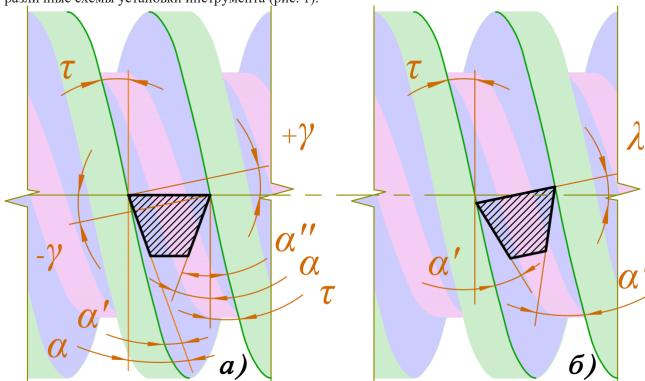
Схемы установки резьбового резца по отношению к заготовке: а) в осевом сечении резьбы; б) в плоскости, нормальной к винтовой поверхности резьбы
